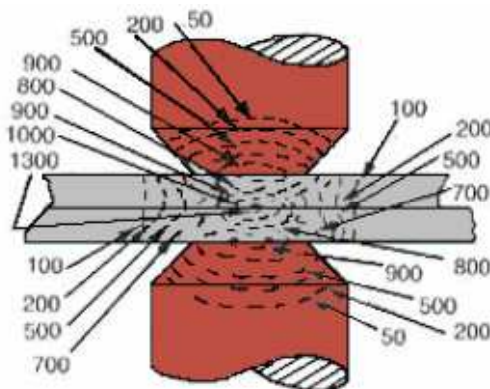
Temperaturas Instantâneas estimadas de soldagem a ponto de chapas de aço em graus Celsius no instante de finalização da soldagem[32].
